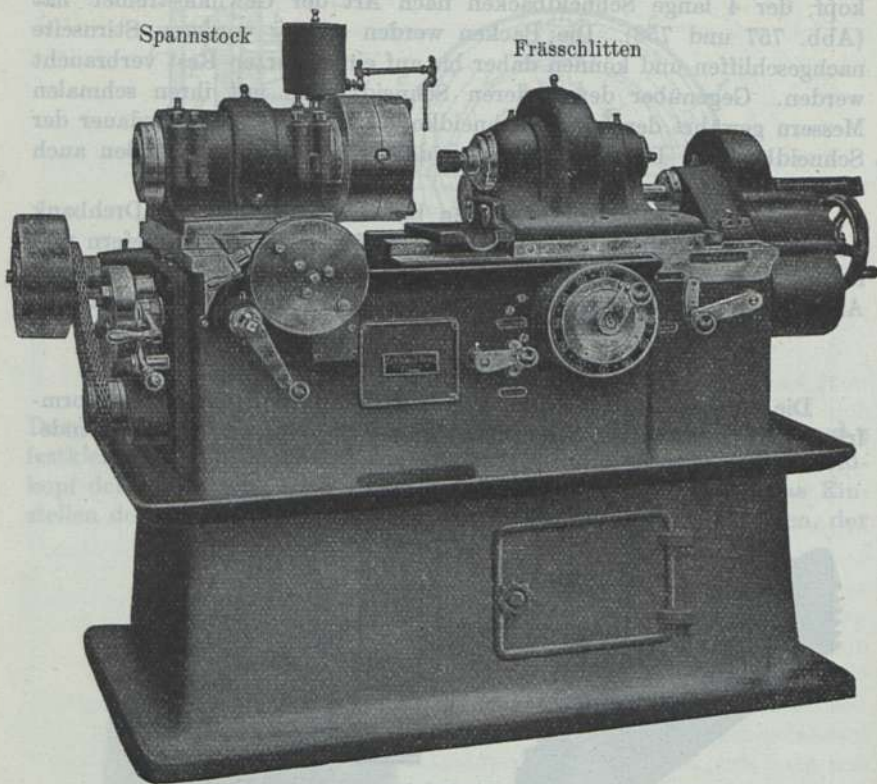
Gewindefräsmaschine. Karl Hasse & Wrede, Berlin N.
